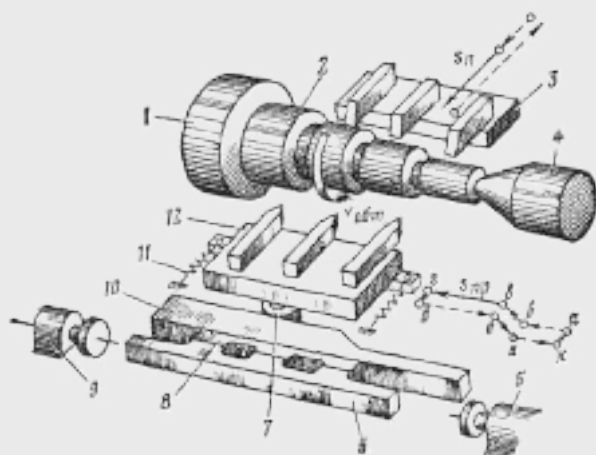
Схема токарного багаторізевого верстата 1730: 1 — передня бабка; 2 — заготовка; 3 — поперечний супорт; 4 — задня бабка; 5, 9 — упор; 6, 8 — планка; 7 — ролик; 10 — лінійка; 11 — пружина; 12 — повздовжній супорт
